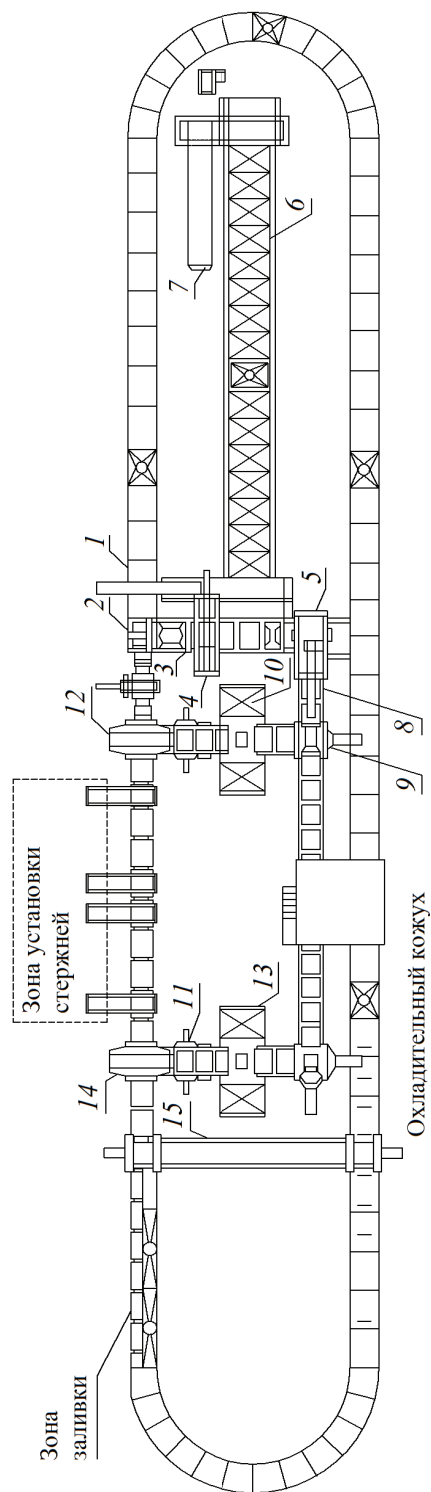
Планировка формовочной линии Л453: 1 – литейный пульсирующий конвейер; 2 – механизм съема форм с литейного конвейера; 3, 8 – роляганги; 4 – механизм выдавливания «кома»; 5 – механизм очистки опок; 6 – транспортер допнительного охлаждения; 7 – выбивные решетки; 9 – распаровщик; 10, 13 – трехпозиционные формовочные машины для формовки нижних и верхних полуформ; 11 – кантователь; 12 – установщик нижних полуформ на конвейер; 14 – сборщик полуформ; 15 – грузоукладчик
